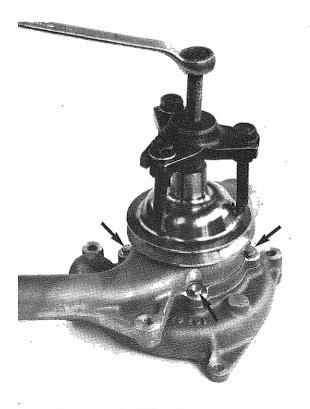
Estrattore n. 19 - Viti fissaggio Puller No. 19 - Screws
